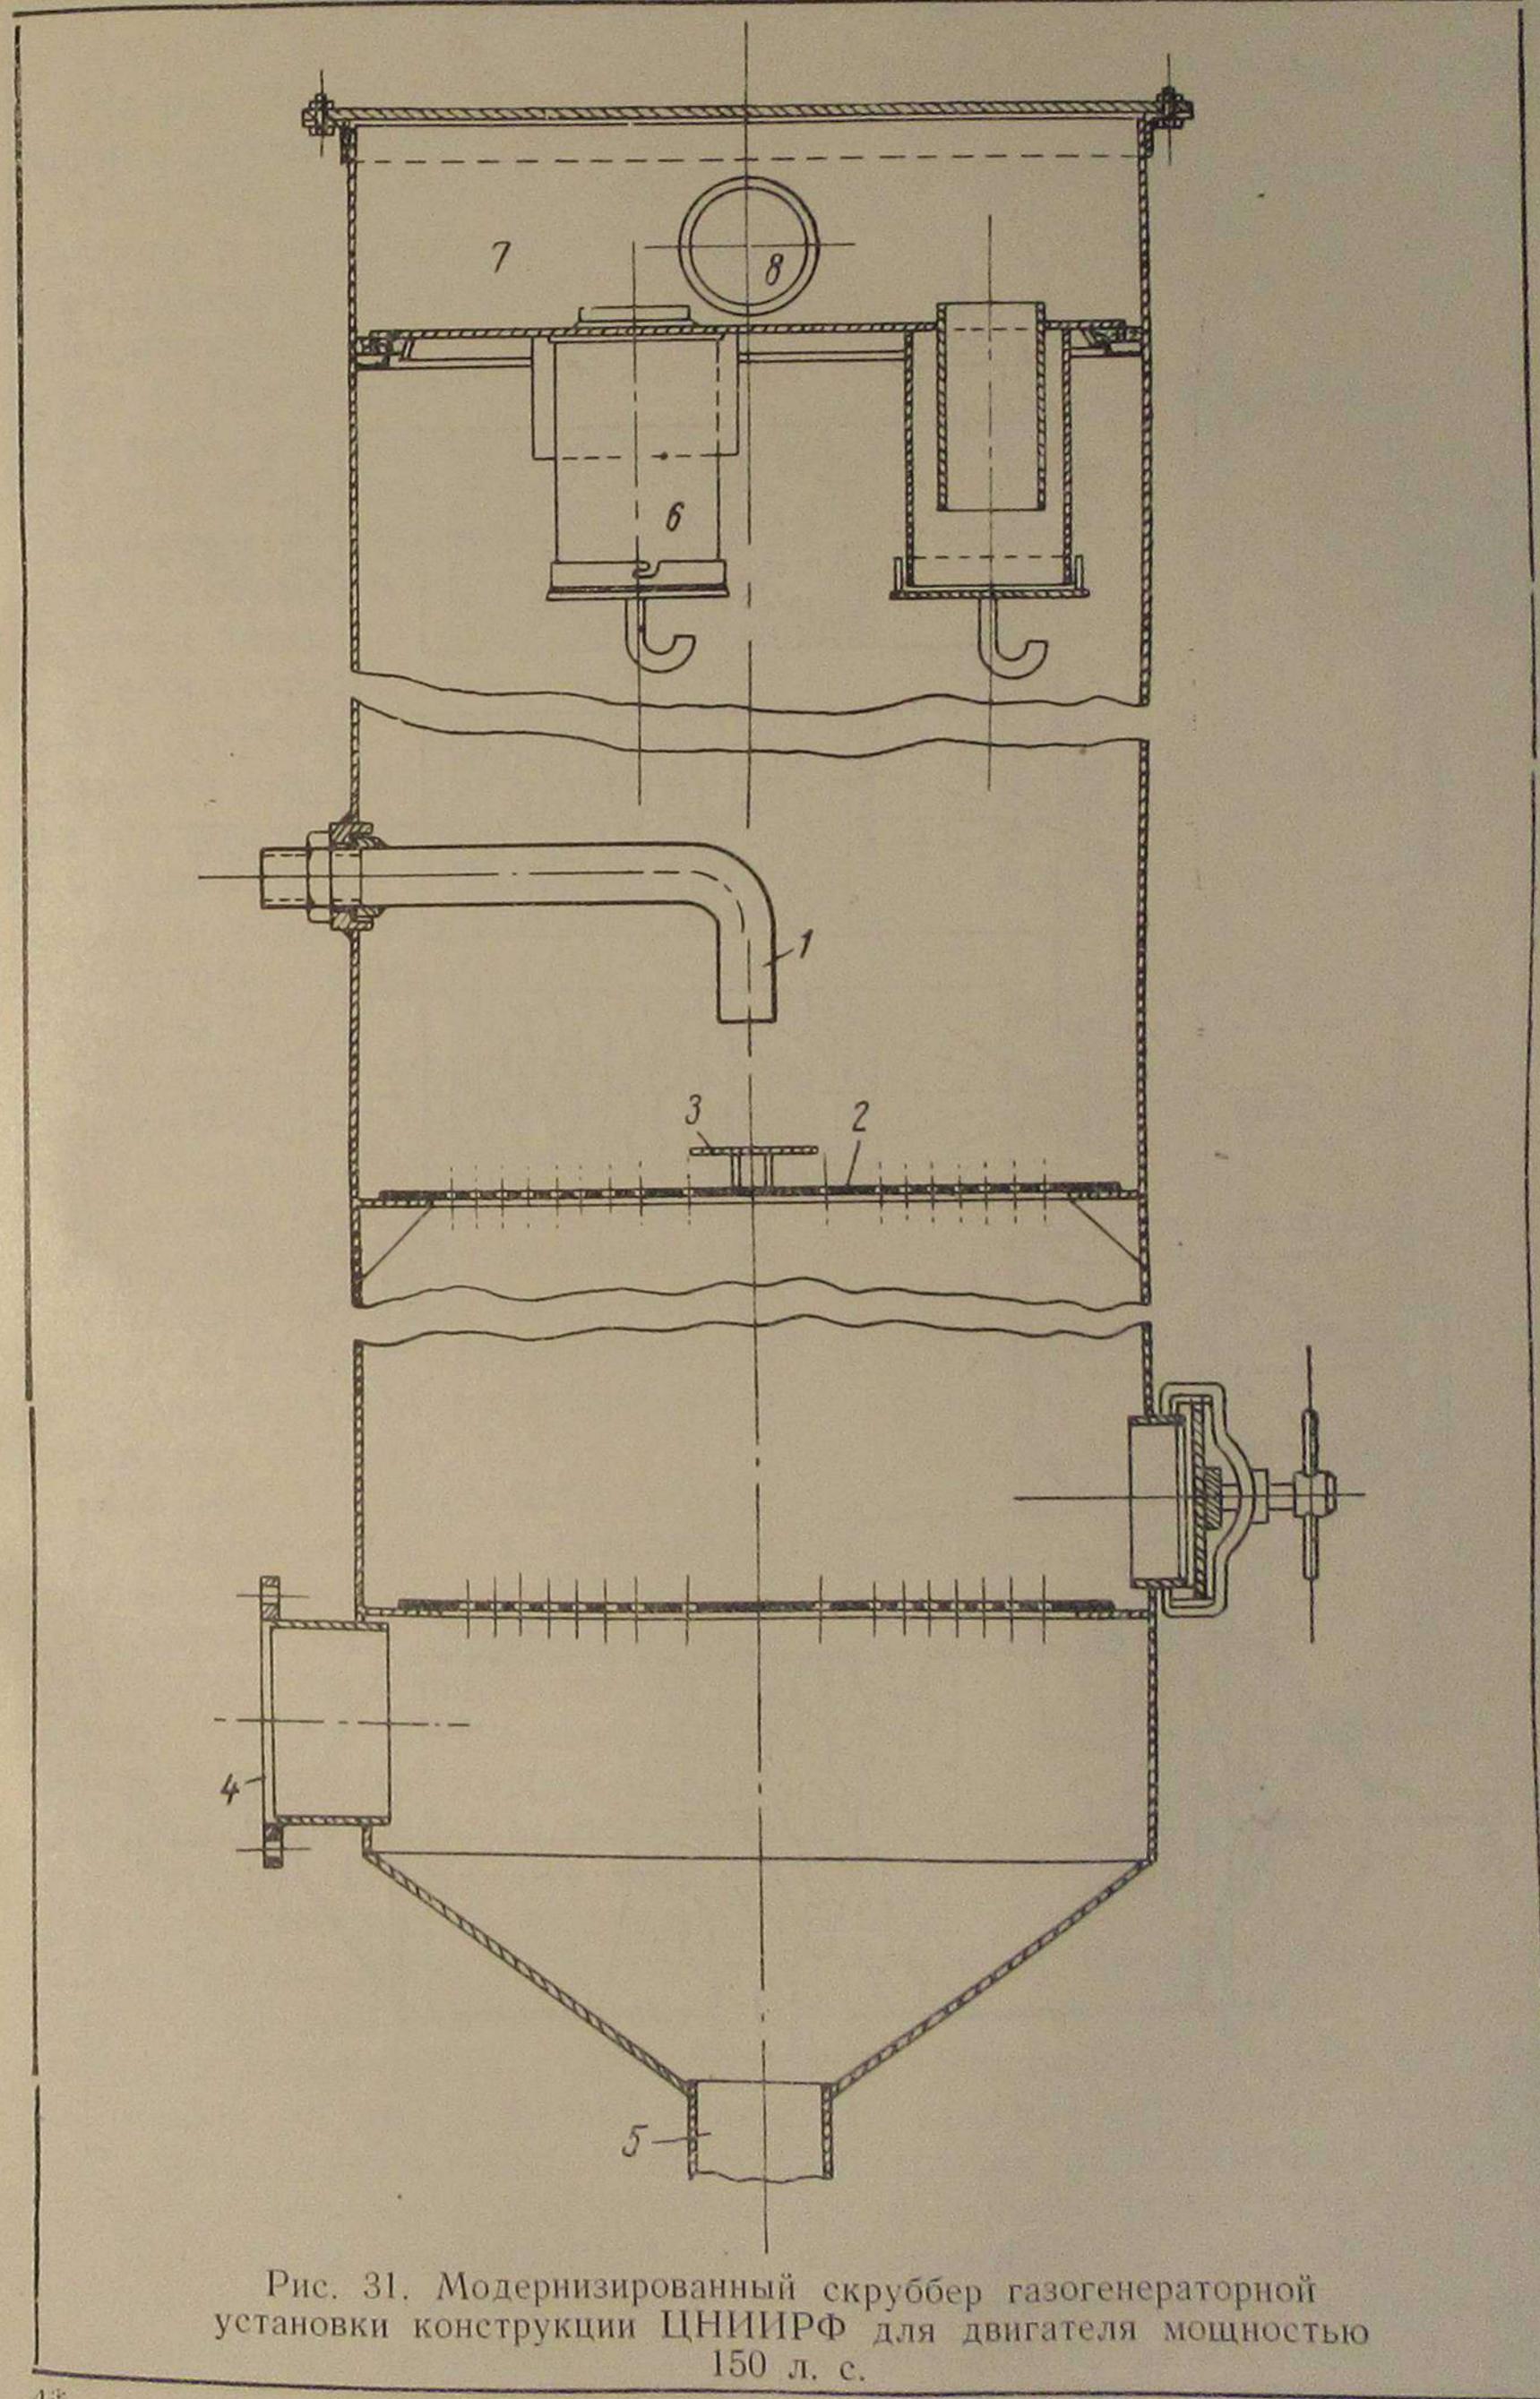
Модернизированный скруббер газогенераторной установки конструкции ЦНИИРФ для двигателя мощностью 150 л. с.
